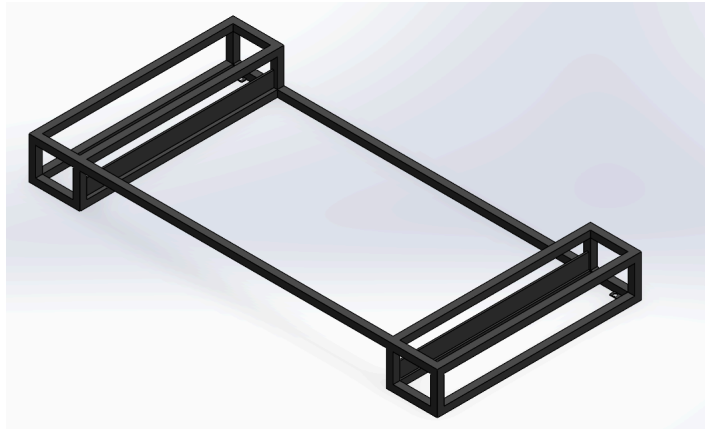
Base estructural del Tablero (Fuente: Elaboración Propia)
